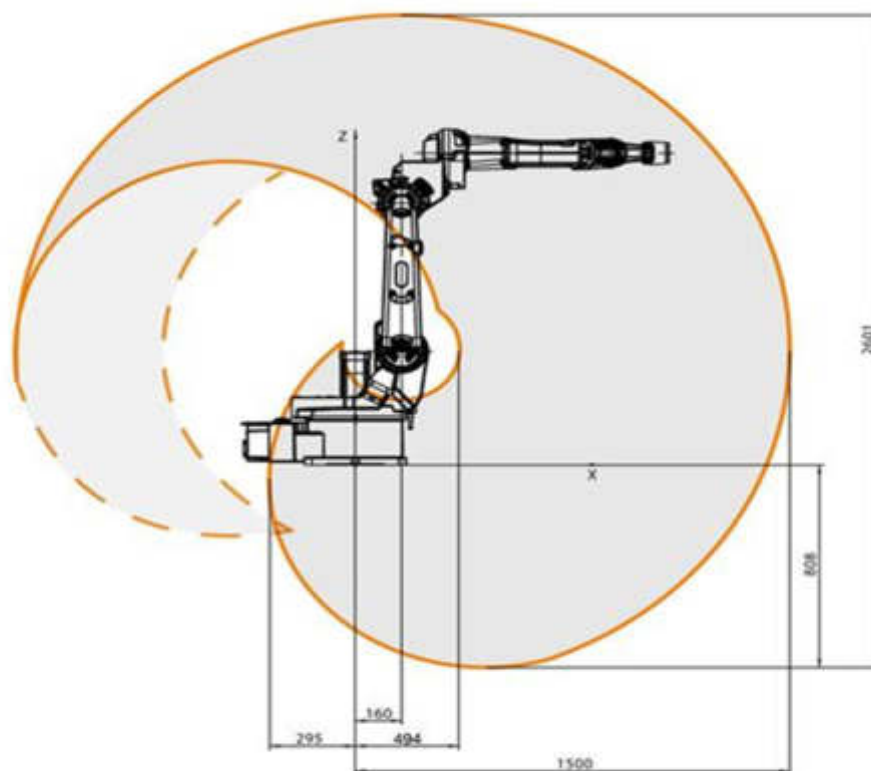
Сварочный робот IRB 1520ID
